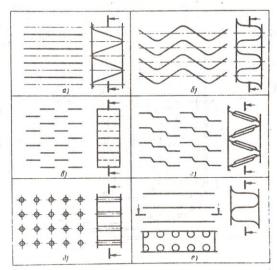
Пластинчаторебристые поверхности с различными типами ребер: а — гладкими; б-волнистыми; в — прерывистыми; г — чещуйчатыми; д— прерывистыми; е — перфорированными.
